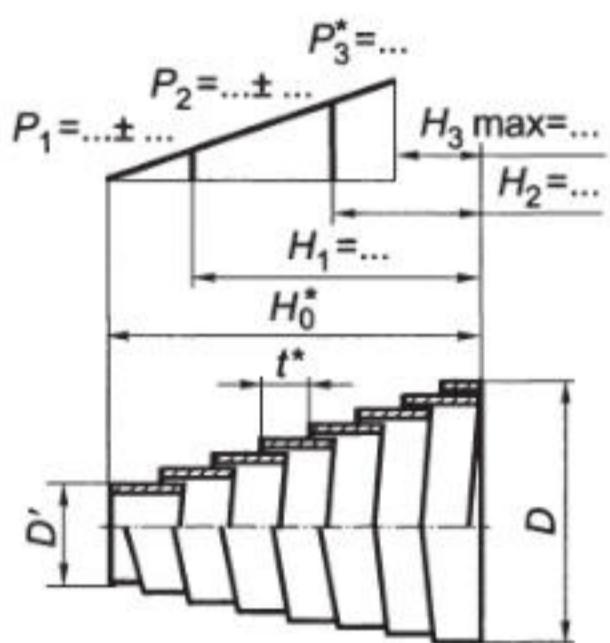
Пружина сжатия коническая (трубчатая) из заготовки прямоугольного сечения с шлифованными на $\frac{3}{4}$ окружности опорными поверхностями
